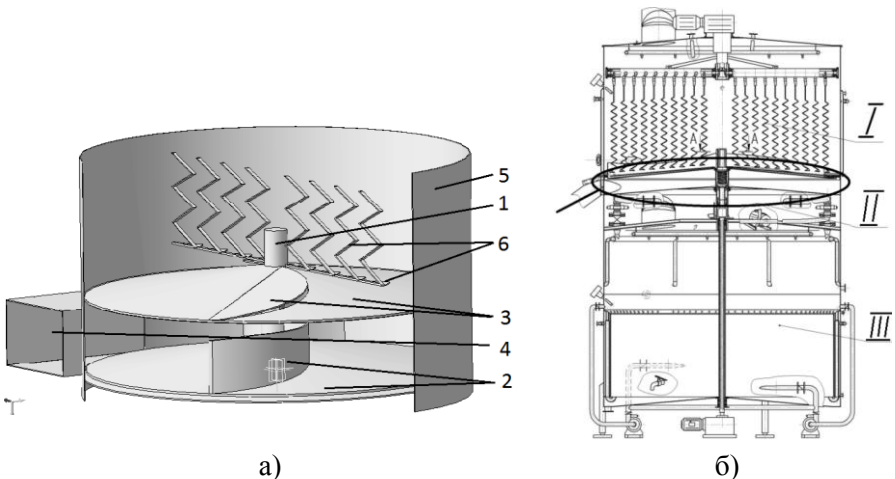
Комбінований варильний агрегат для приготування пивного сусла (б) та розріз заторно-фільтраційного апарату (а): 1-привідний вал; 2- диск-мішалка; 3- фільтрувальний каркас із фільтруючими сегментами; 4- вивантажувальний патрубок; 5- корпус апарату; 6- плужки розрихлювачі
